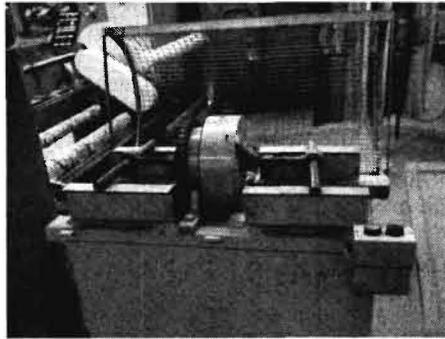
Gerät zur Demontage, Aufarbeitung und Montage von Spurstangen
